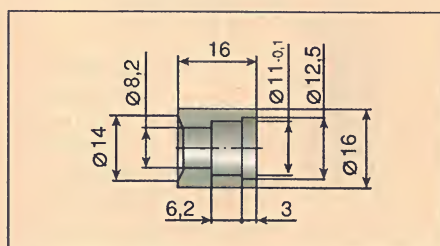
Оправка для запрессовки направляющих втулок клапанов "Ауди-100".
